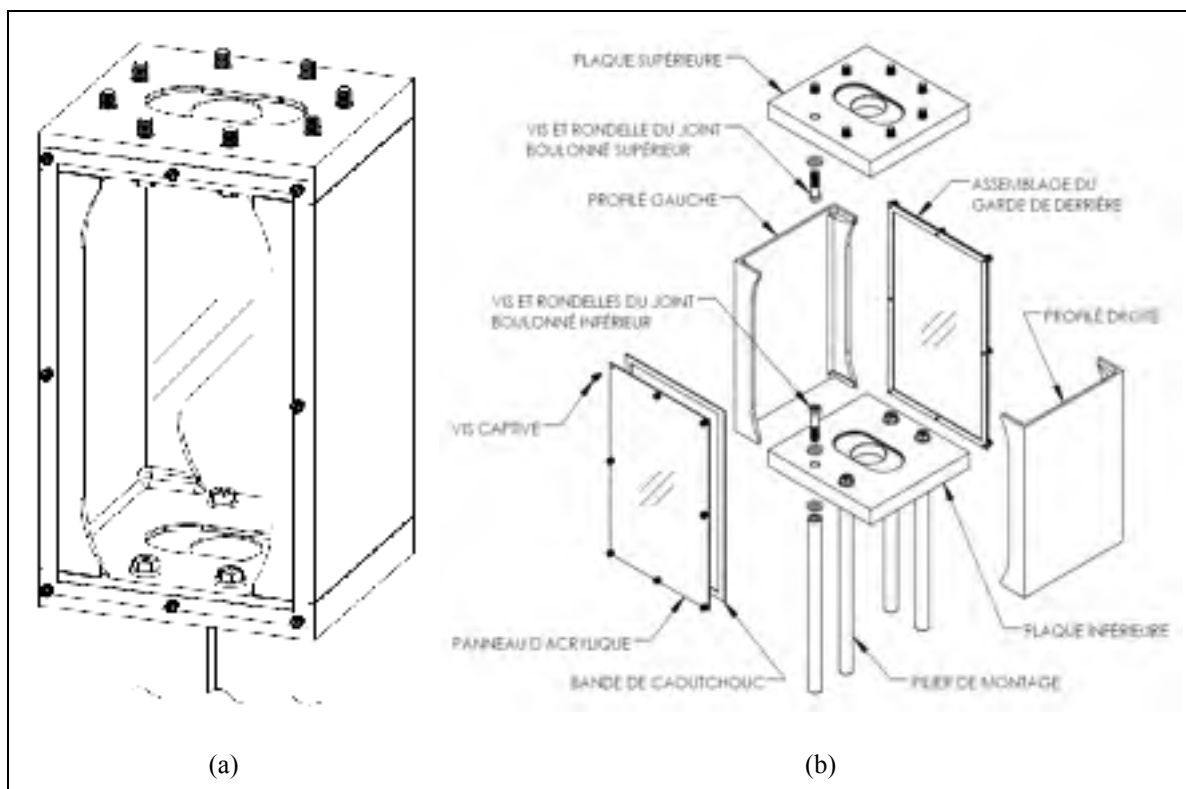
Représentation du concept final de piédestal assemblé (a) et en vue explosée (b)
